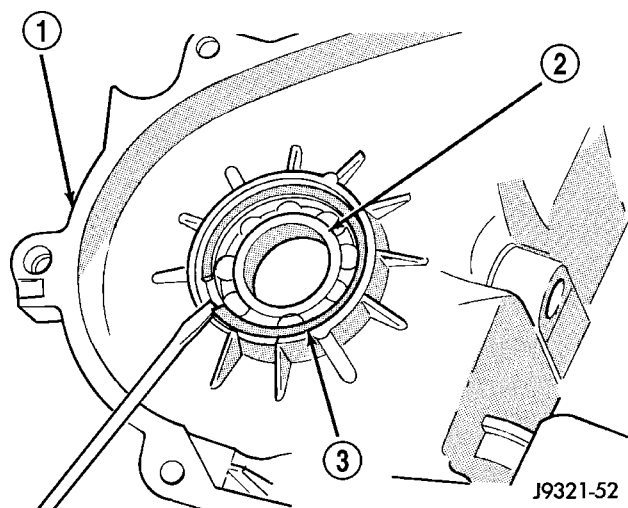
Desmontaje del anillo de muelle del cojinete del eje transmisor delantero
